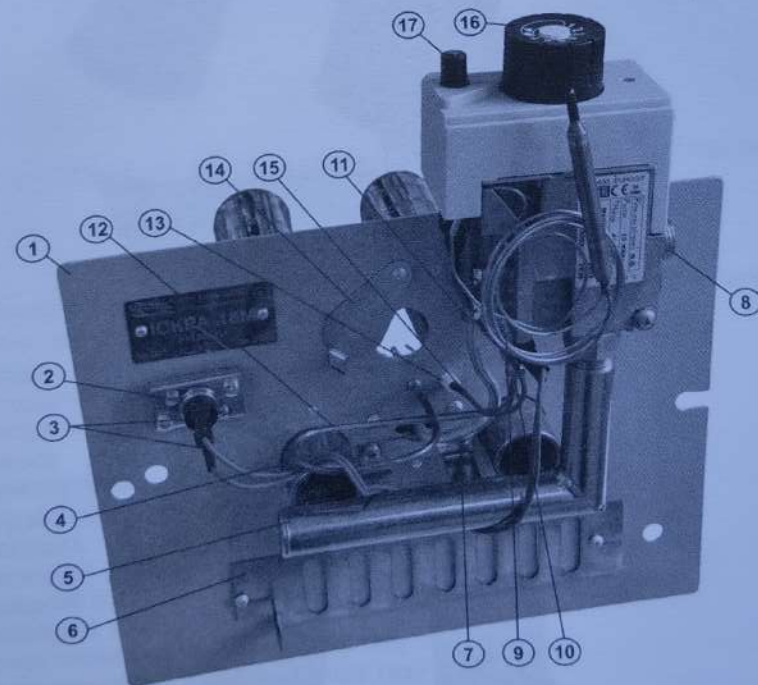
Пристрій газопальниковий ІСКРА (вид спереду)
